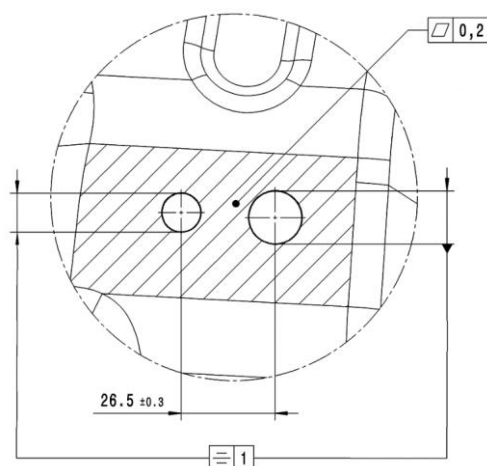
Pormenor da zona exterior da base do reforço interior com furação dupla
